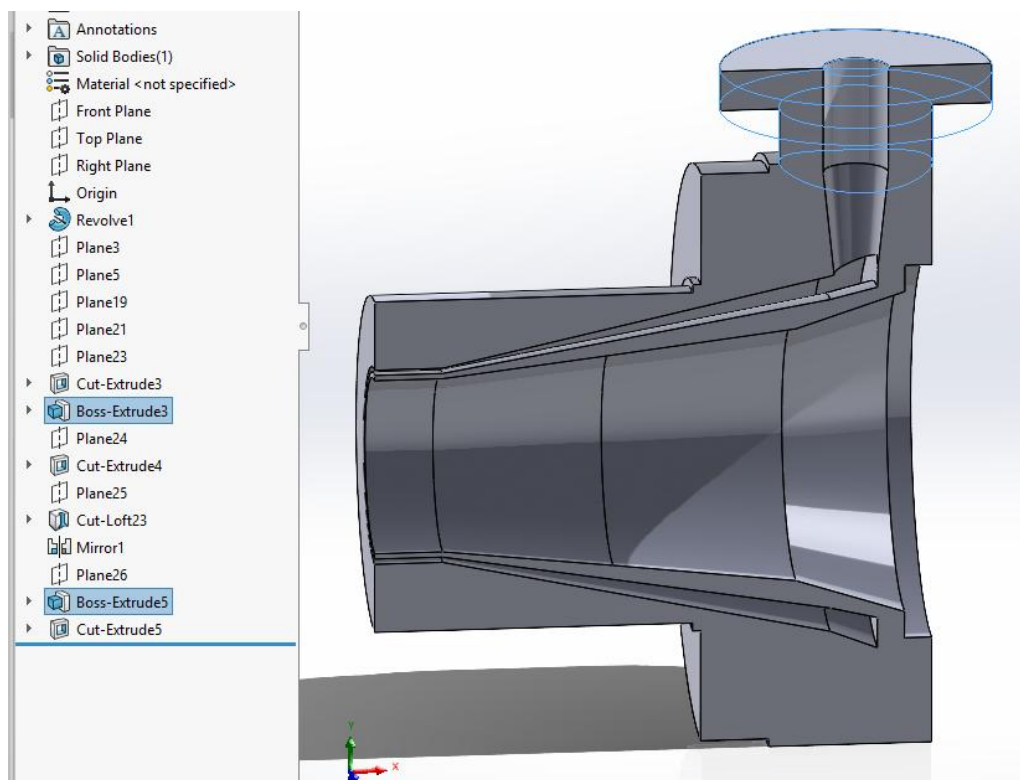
Корпус та фланець додаткового каналу, «Boss Extrude»
